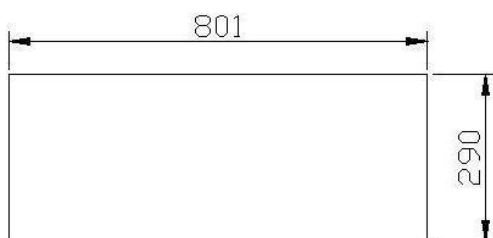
Construcción de la sección cilíndrica del reactor de metoxido.
